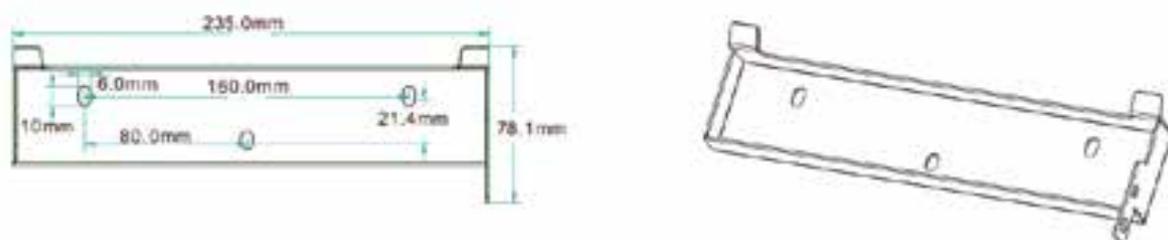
Dimensões do suporte de SOFAR 1-4KTL2-G3
